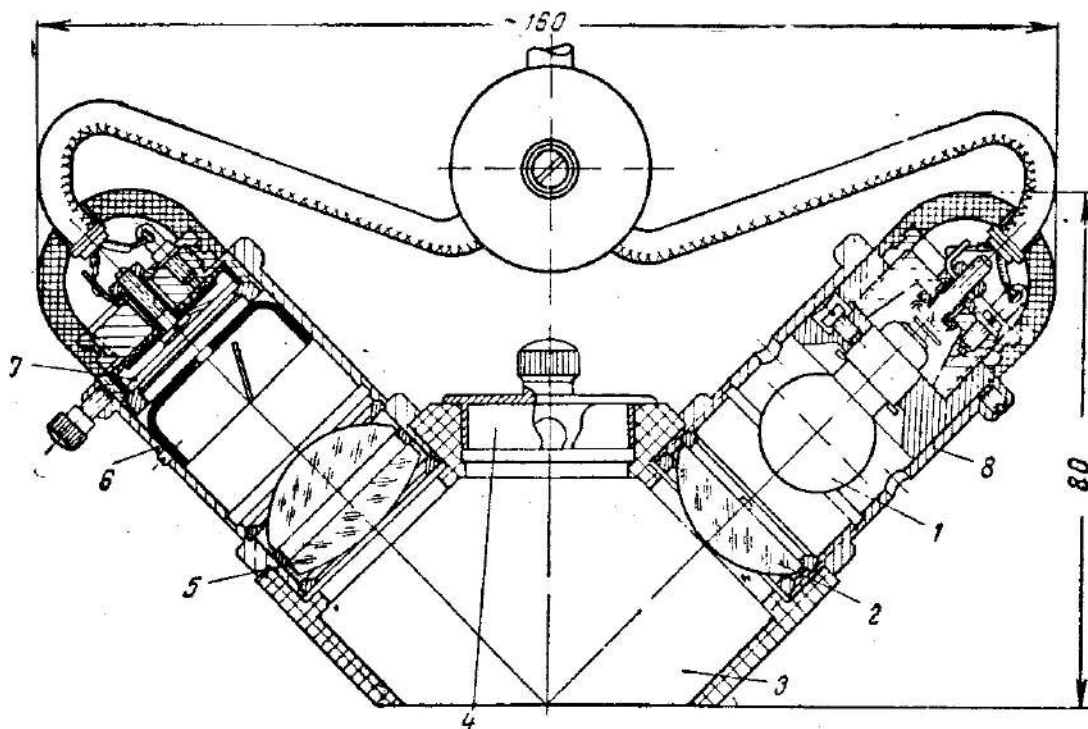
Измерительная головка фотоэлектрического блескомера ФБ-2: 1 — лампа осветителя; 2 — линза; 3 — корпус; 4 — крышка; 5 — конденсор; 6 — тубус фотодатчика; 7 — фотоэлемент; 8 — тубус осветителя.
